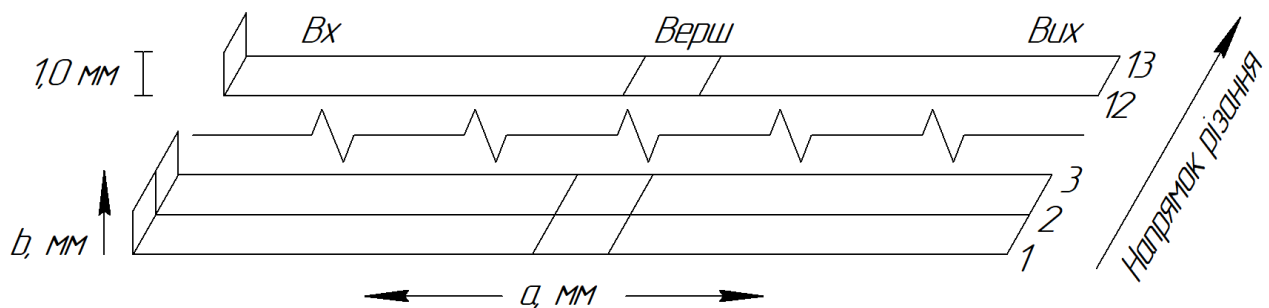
Номінальні площини перетинів зрізів черв'ячного зубофрезерування
